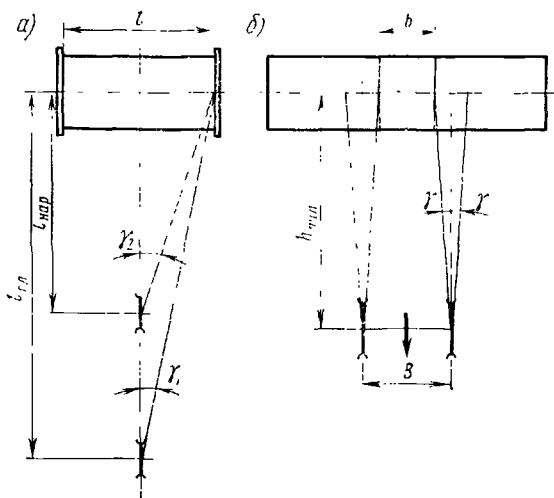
Допускаемые углы набегания каната на барабан
